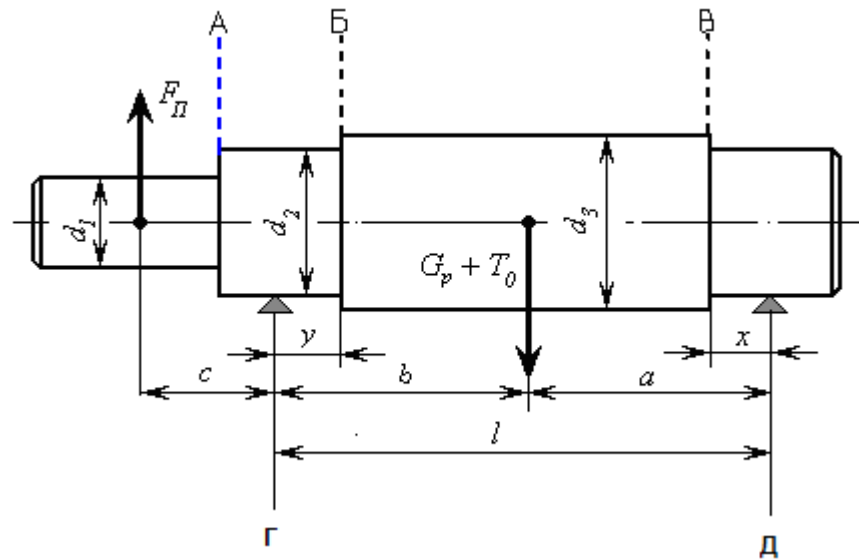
Конструкция и основные размеры вала для механического расчёта
